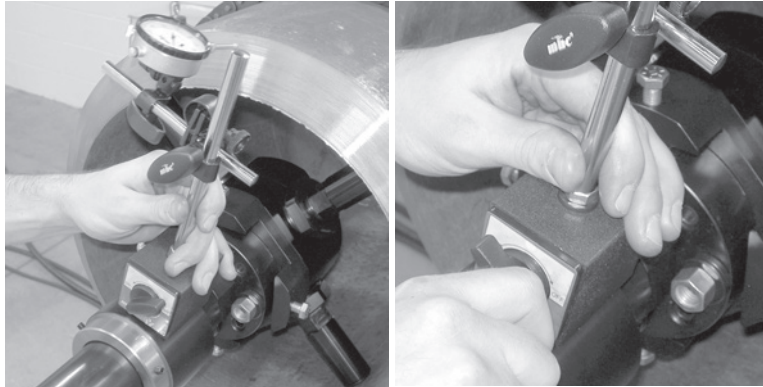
Installare la base magnetica dell'indicatore sul collare e accendere l'interruttore per attivare il magnete.
